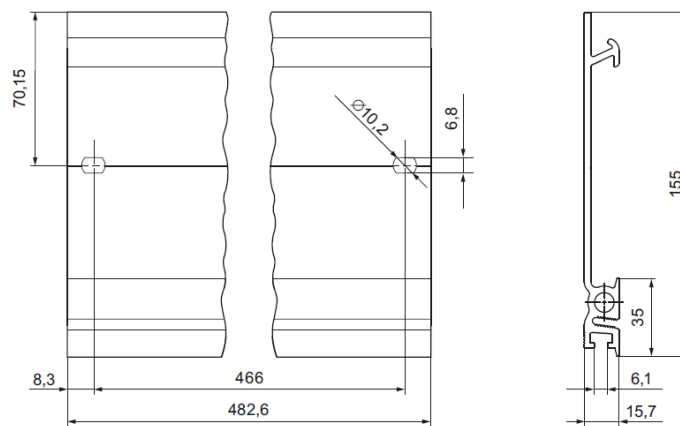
Dimensões em milímetros da calha de montagem considerada (*6ES7590-1AE80-0AA0*) fornecida pela entidade *Siemens* [26].
